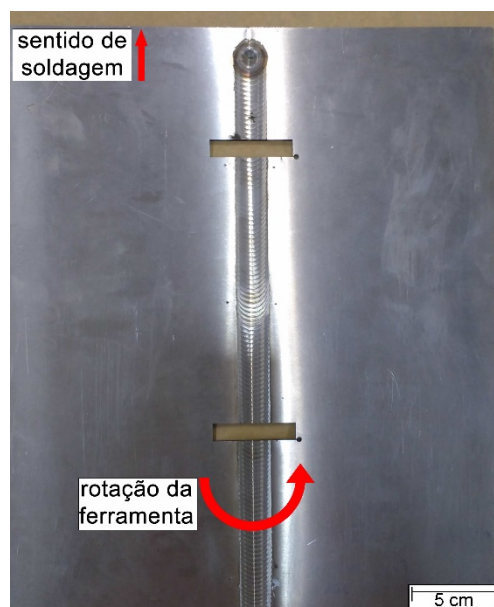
Junta soldada do AISDs UNS S32760 como recebida.
